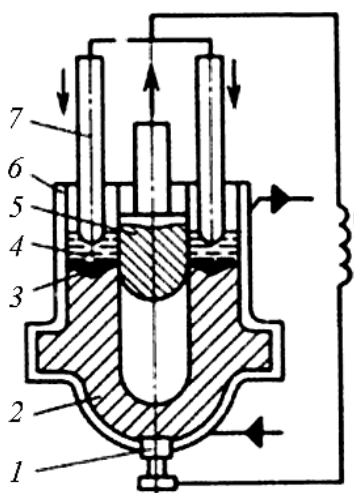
Схема изготовления отливок электрошлаковым литьем
